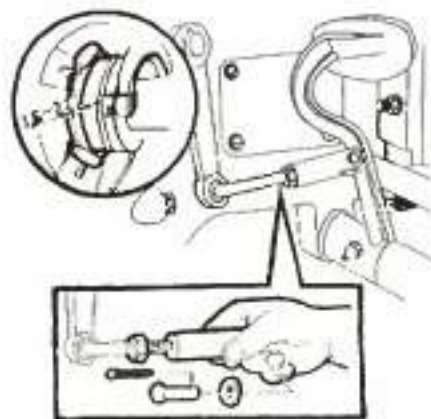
Регулировка свободного зазора муфты сцепления и свободного хода педали
